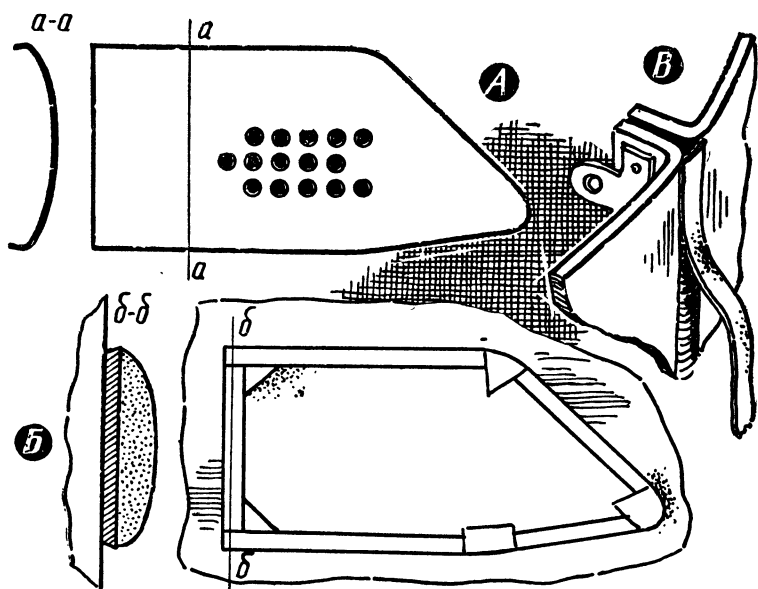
Изготовление детали корпуса снегохода; А — общий вид; Б — болван; В — крепление деталей.
